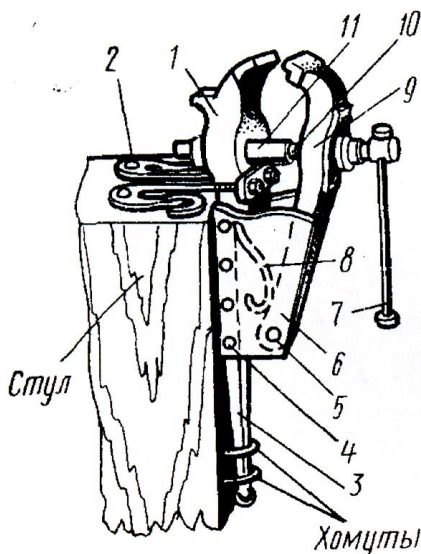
Стуловые тиски: 1 – неподвижная губка; 2 – крепежная планка; 3 – нижний стержень; 4 – заклепки; 5 – шарнир; 6 – накладка; 7 – рукоятка; 8 – пружина; 9 – подвижная губка; 10 – винт; 11 – гайка
